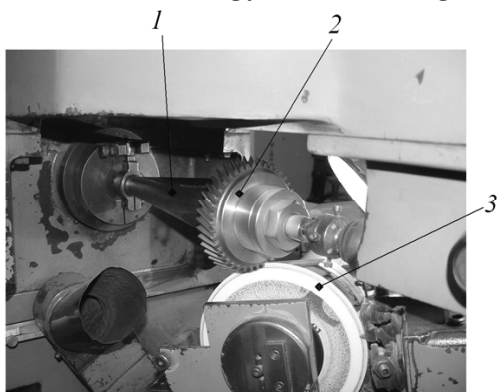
Шлифование профиля зубьев долбяка: 1 – оправка; 2 – заготовка долбяка; 3 – шлифовальный круг
